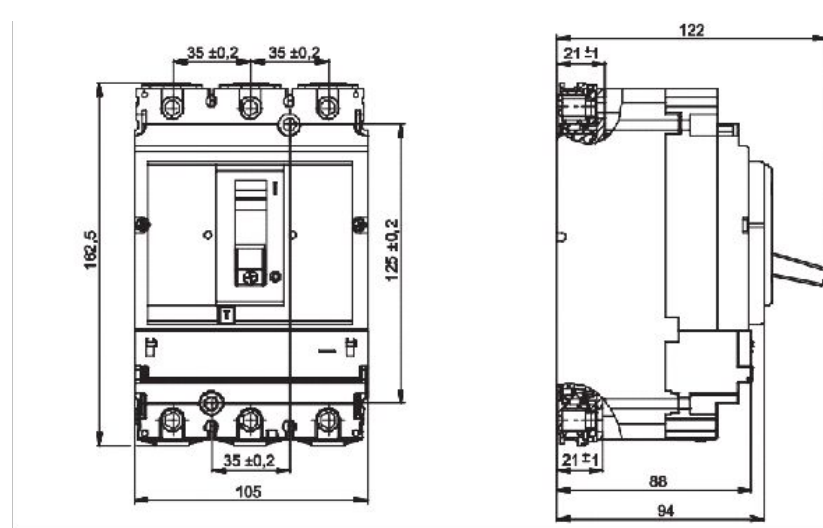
Габаритные, установочные и присоединительные размеры выключателя
